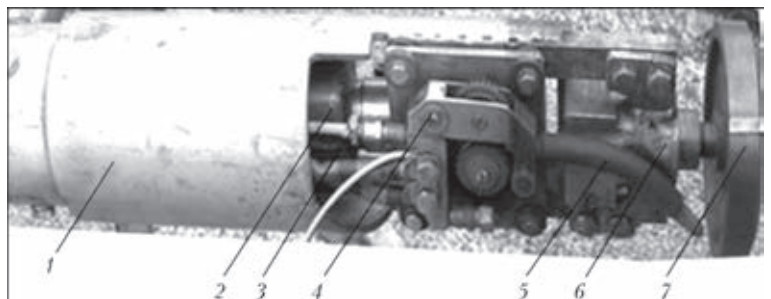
Автомат для сварки в стесненных условиях на большой глубине: 1 — корпус; 2 — механизм вращения; 3 — направляющий канал; 4 — подающий механизм с колебателем мундштука; 5 — мундштук; 6 — крепление и элементы токопередачи на доньшко; 7 — доньшко
